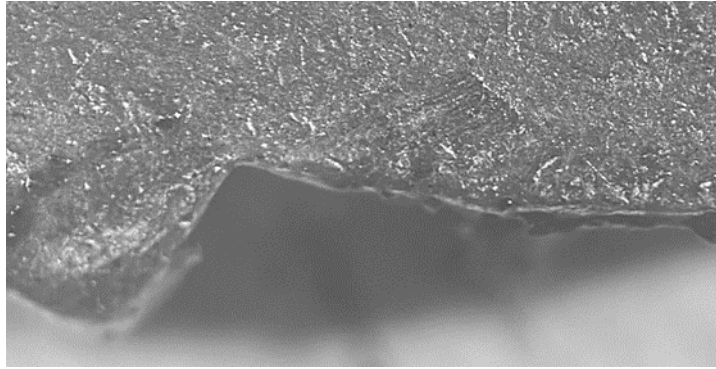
Динамический след, расположенный на поверхности основного диска около выступа для фиксации в роторе у внешнего края
